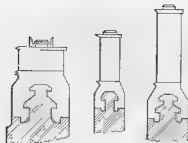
Рабочие лопатки 1, 7 и 10-й ступеней ротора высокого давления
